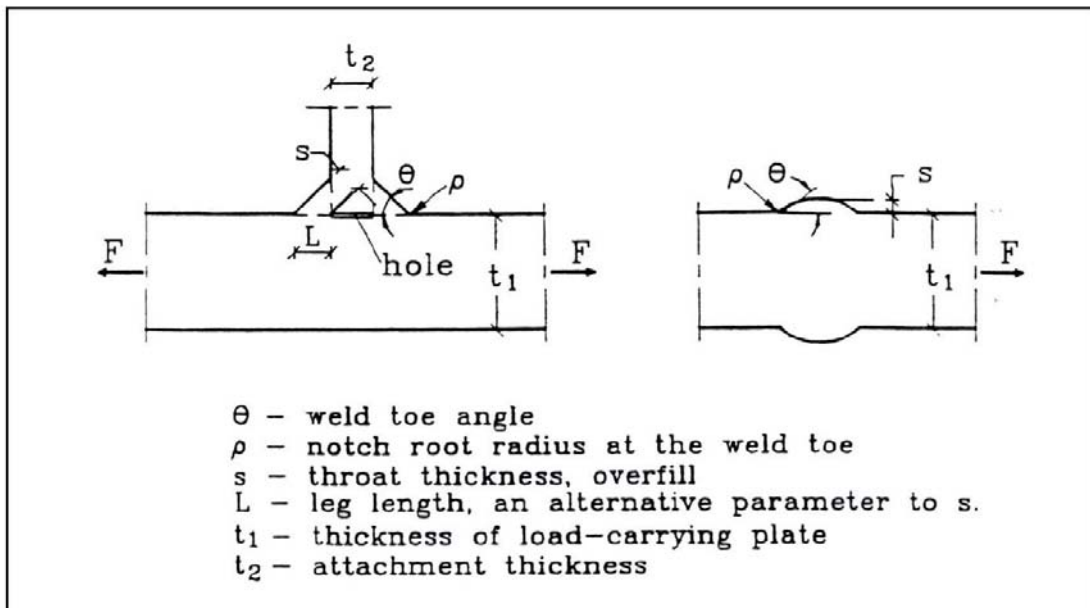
paramètres caractérisant la géométrie des assemblages soudés [IB94]
